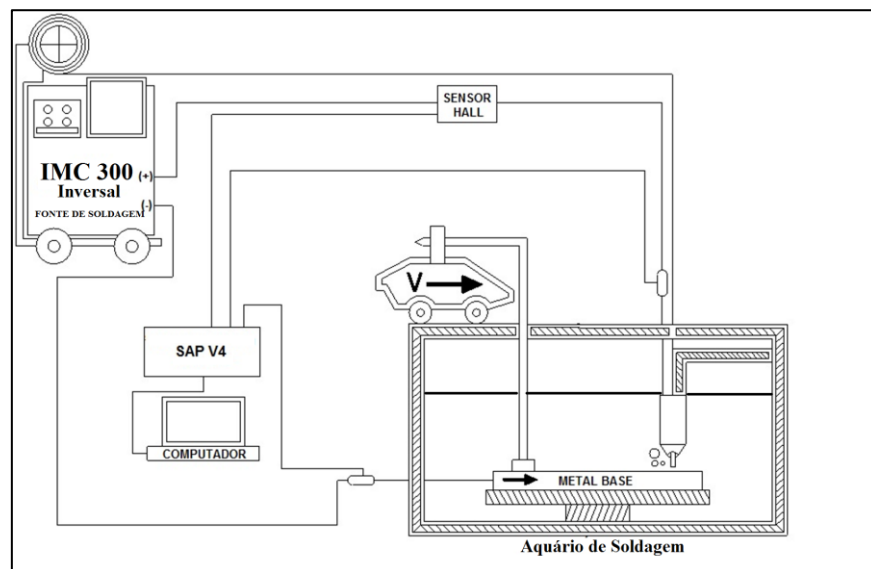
Montagem do processo de soldagem e aquisição de dados.
